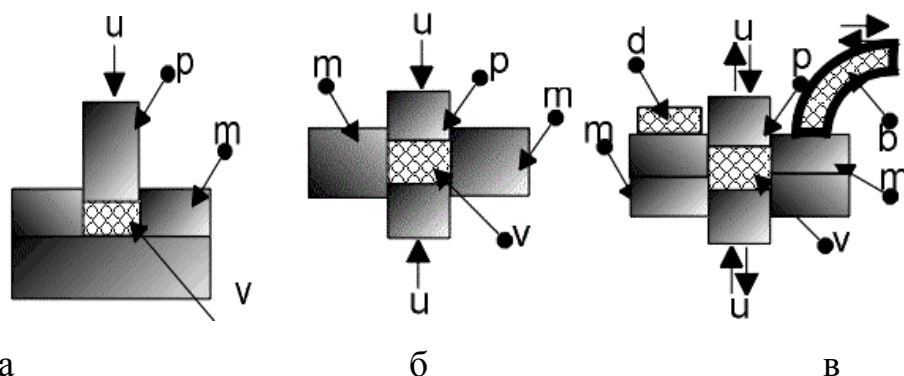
Различные варианты прессования: а – прессование с одним пуансоном; б – прессование с двумя пуансонами; в – прессование с автоматически заполнением пресс-формы и выталкиванием готовой прессовки (u – направление усилия, m – матрица пресс формы, p – пуансон, v – прессуемое вещество (порошок), b – бункер-питатель, d – спрессованная деталь) [7]
